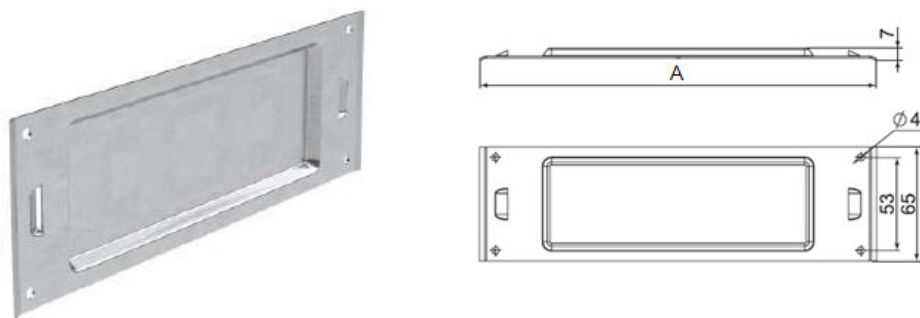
Пластина защитная IP44 (металл), типов: 30570, 3058
